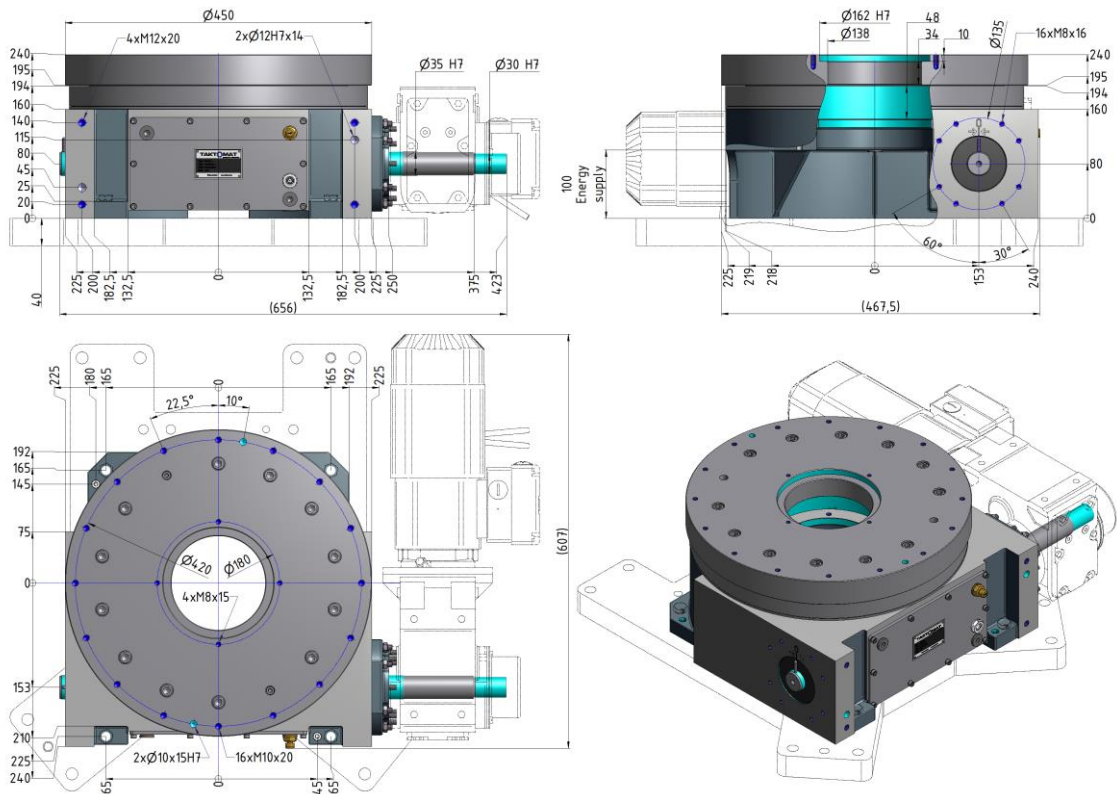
Hoja de dimensiones TMF 1000 adaptiert horizontal
